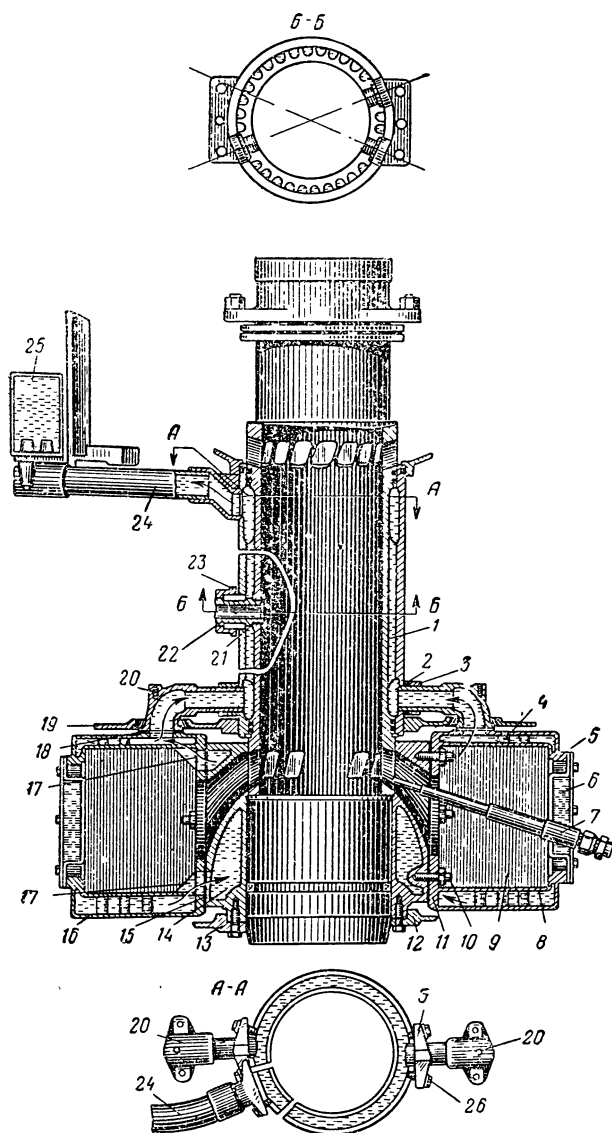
Выпускные коллекторы, выпускная коробка и водяное охлаждение гильзы цилиндра:
